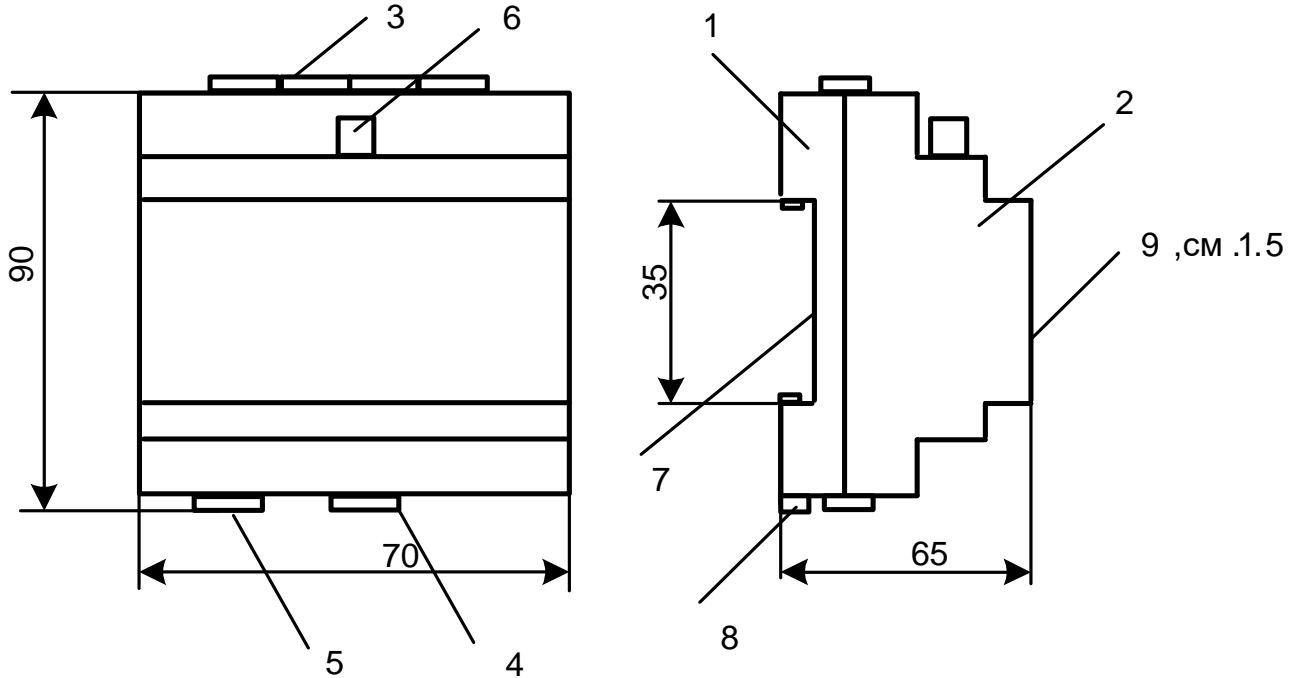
габаритные и установочные размеры преобразователя ЧИС исполнения «в корпусе DIN 20»
